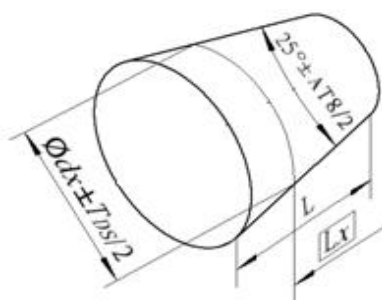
给定截面圆锥直径公差和圆锥角公差의注法
